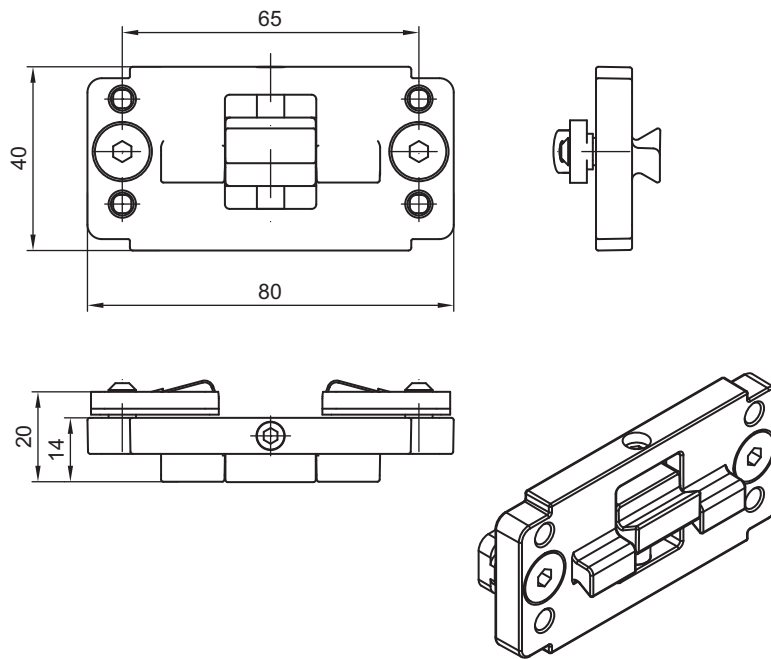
Supporto di serraggio BT-P40 per il fissaggio nelle colonne di fissaggio UDC
